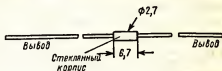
Внешний вид и габаритные размеры варикапов коротковолновой серии.
